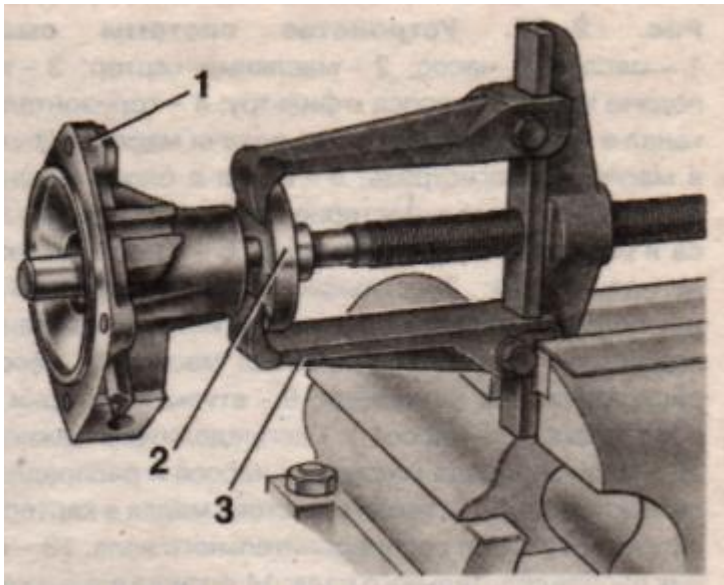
Зняття маточини шків: 1 - кришка корпусу насоса; 2 - маточина шків; 3 – знімач виверніть стопорний гвинт 9 (мал.4.2) і вийміть підшипник з валиком насоса; видаліть сальник 11 із кришки 2 корпусу
